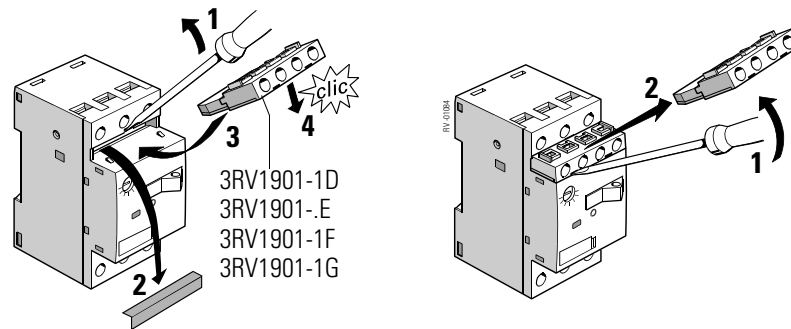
Querliegender Hilfsschalter, Montage (Beispiel: Baugröße S00)
